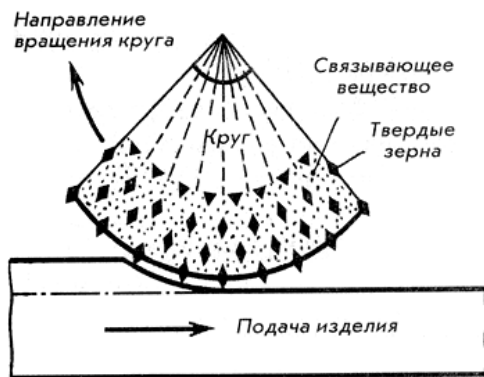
Процесс обработки заготовки шлифовальным кругом
